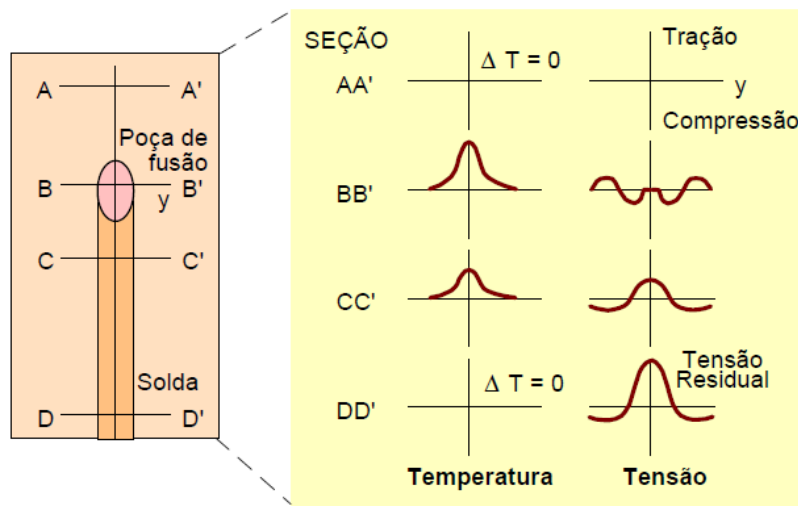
Desenvolvimento de tensões longitudinais durante a soldagem.
